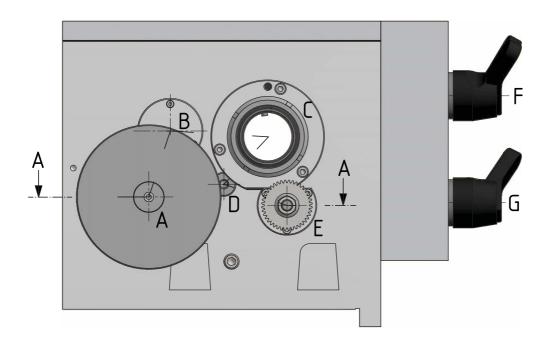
Getriebe Spindelstock 1-6 - Headstock gear 1-6
